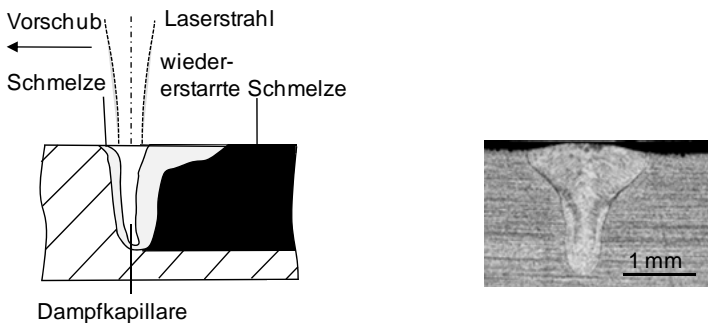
Skizze des Laserstrahl-Tiefschweißens im Längsschnitt (links) und TS-Schweißnahtquerschnitt (rechts); $P_L = 2000 \text{ W}$, $v = 2 \text{ m/min}$, $r_s = 0,3 \text{ mm}$, $\lambda = 1070 \text{ nm}$, Edelstahl 1.4541
